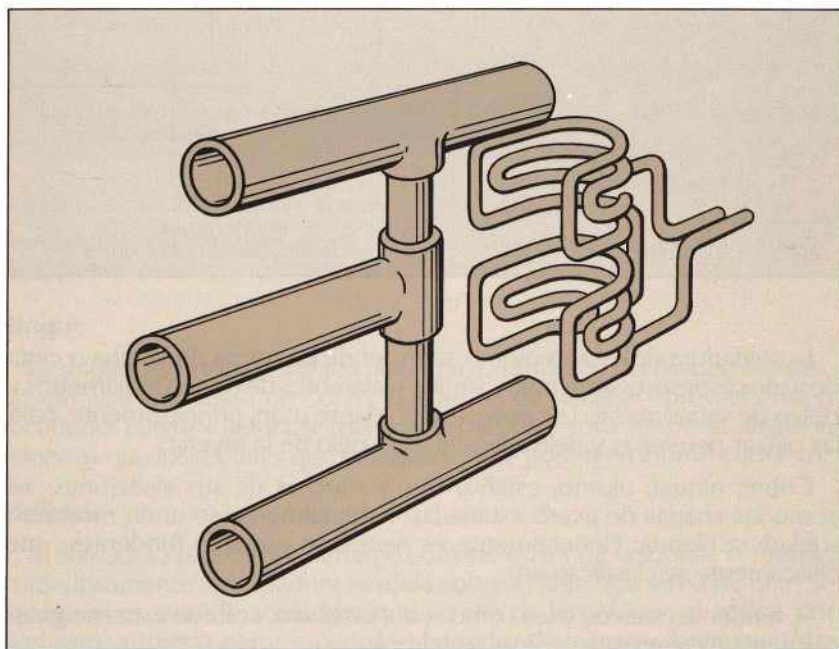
Calentamiento por inducción utilizado para la soldadura dura.
